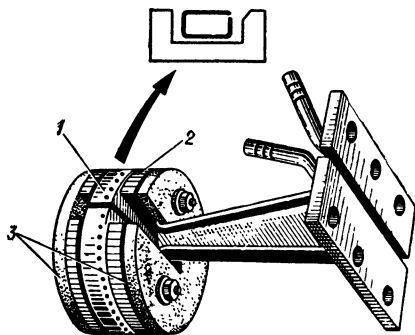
Индуктор для заделки внутренней цилиндрич. поверхности непрерывно-последовательным способом: 1 — индуктирующий провод с отверстием на ребре для выпуска закалочной воды; 2 — магнитопровод; 3 — изоляц. шайбы для крепления магнитопровода.
